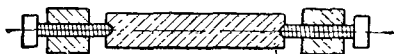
Крепление кварцевой пластинки с боковыми канавками.
